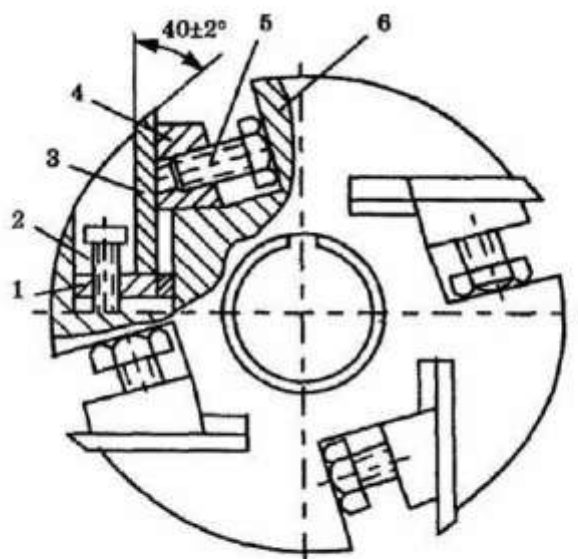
Ножевая головка: 1 - планка; 2 - регулировочный винт; 3 - нож; 4 - прижимная планка; 5 - распорный винт; 6 - корпус головки
